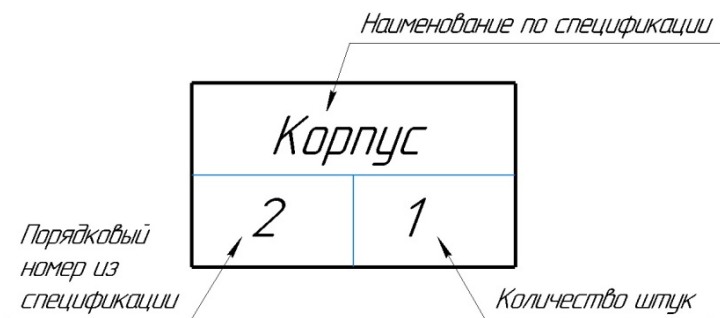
Пример оформления блока базовой детали в схеме сборки
